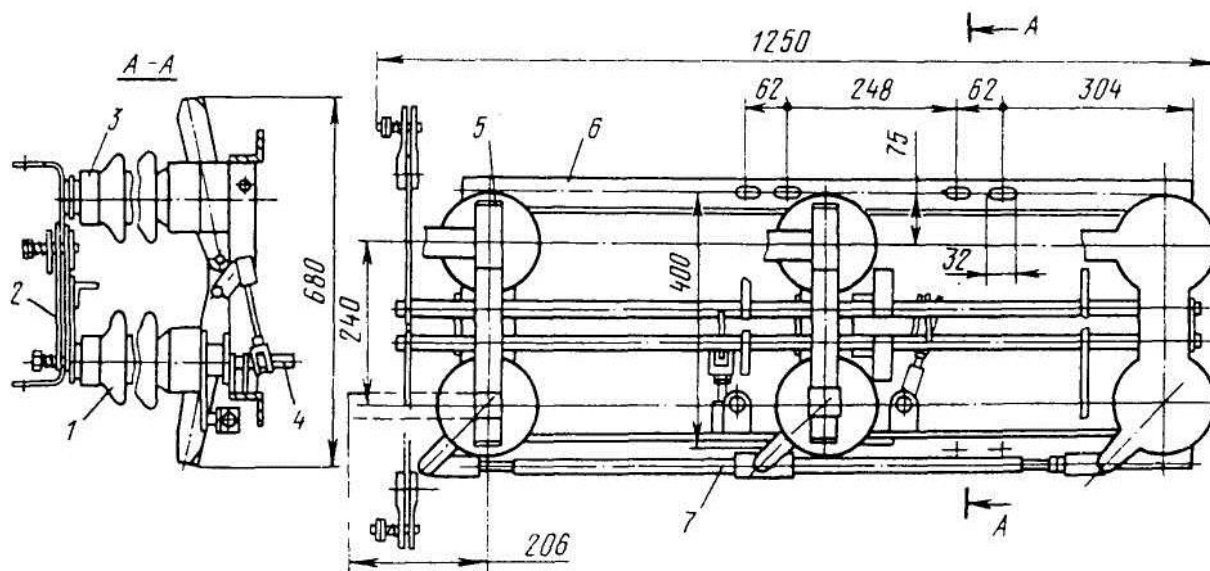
Разъединитель наружной установки типа РЛНД–10
